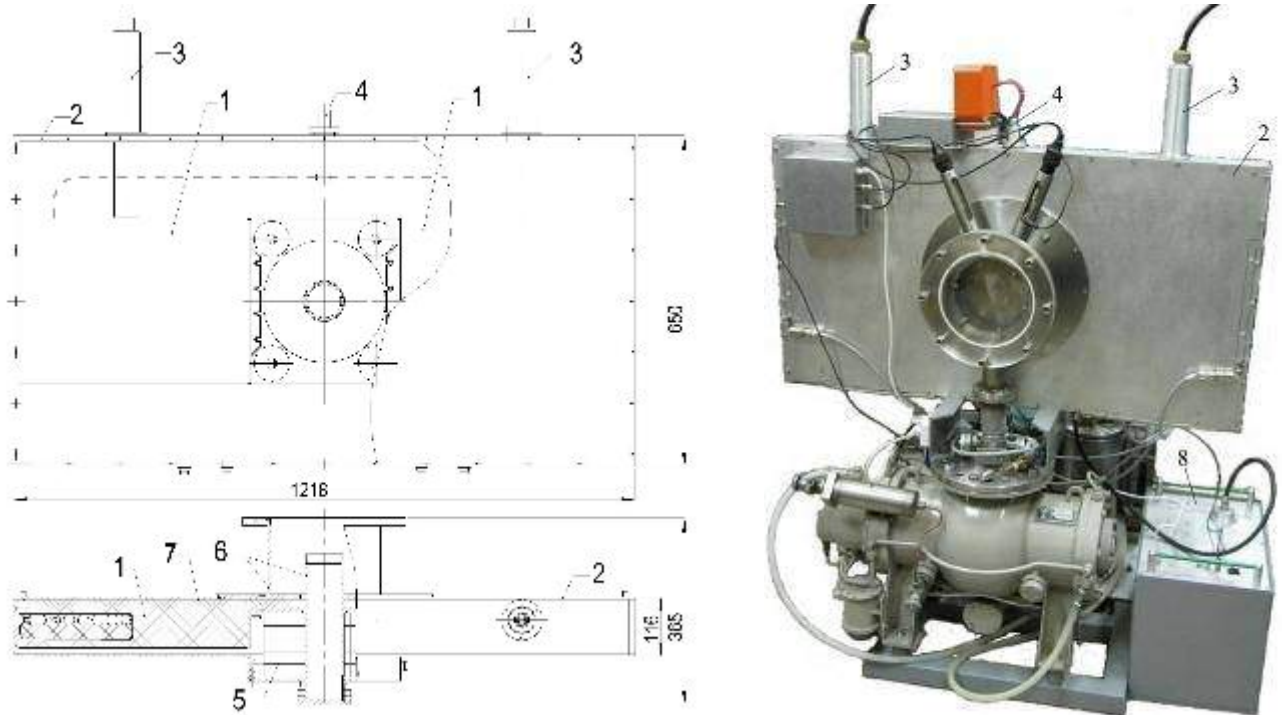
Конструкция и фотография генератора: 1 – секции 80 нФ; 2 – корпус генератора; 3 – высоковольтный ввод; 4 – ввод пускового напряжения; 5 – ферромагнитный сердечник; 6 – выходной вакуумный коаксиал; 7 – проходной изолятор воздух-вакуум; 8 – генератор подмагничивания
